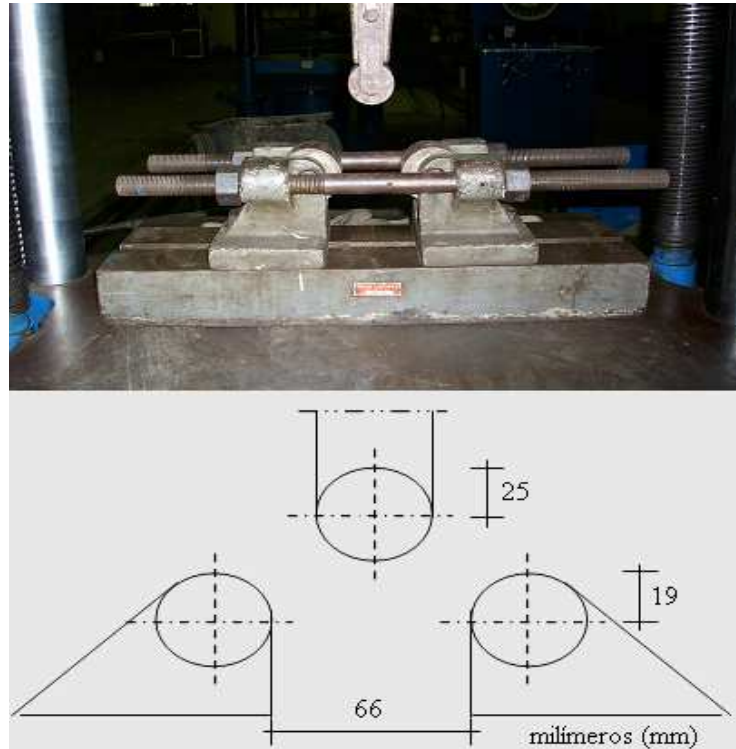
Arriba. Rodillos de la Máquina Universal de Ensayos BALDWIN, utilizada en los ensayos de doblé de la junta soldada. Abajo, dimensiones de los rodillos utilizados para el ensayo de doblé, según lo especificado en QW- 466.1 del Código ASME, Sección IX.
